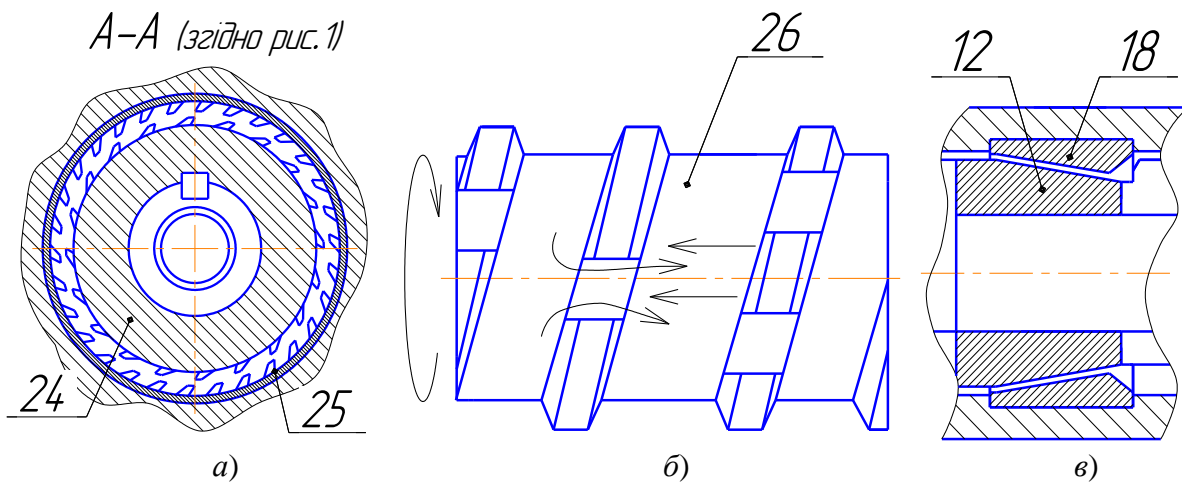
Робочі органи екструдера модернізованої конструкції:
